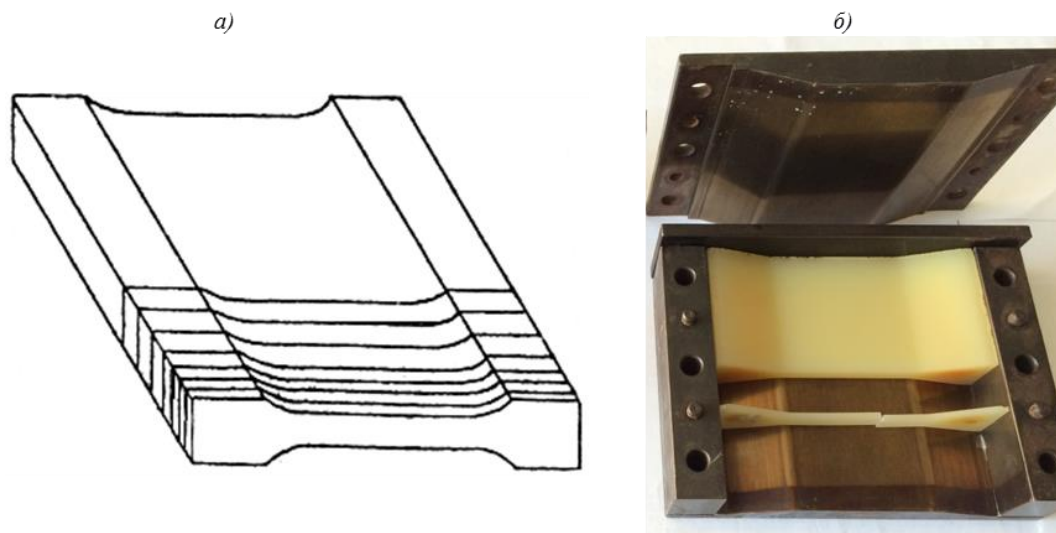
Схема разрезки полимерного блока на образцы для испытаний при растяжении (а) и оснастка для изготовления полимерного блока (б) [7]
